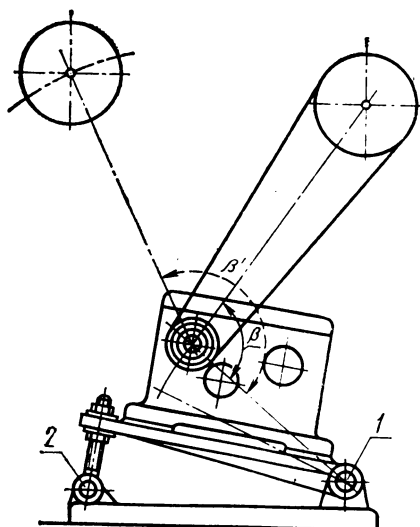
Натяжное устройство с качающейся плитой и резьбовой стойкой
